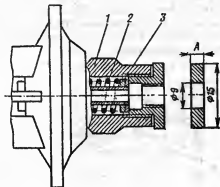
Установка дополнительной шайбы в вакуумный регулятор:
